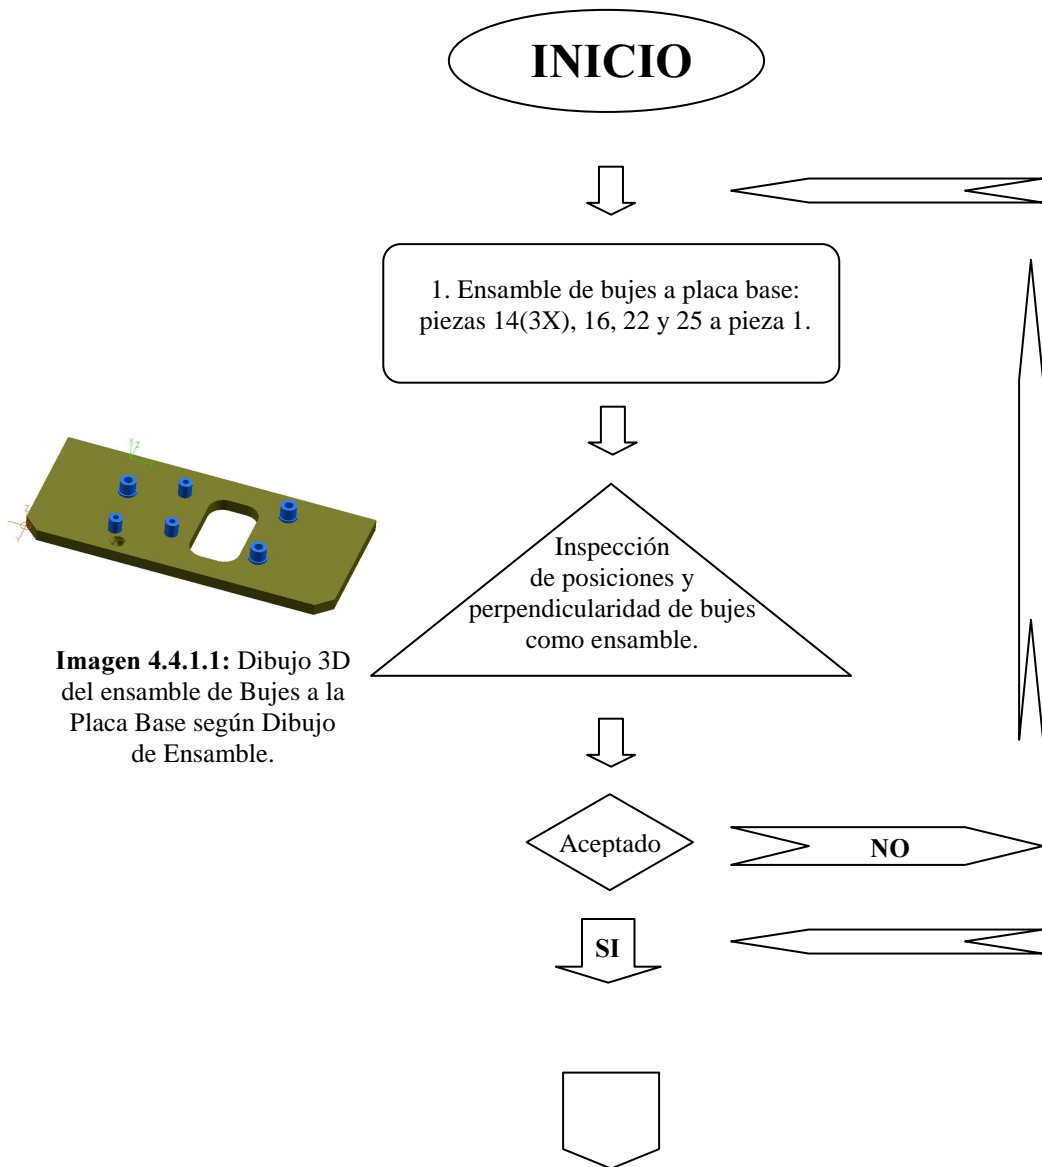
Dibujo 3D del ensamble de Bujes a la Placa Base según Dibujo de Ensamble.
